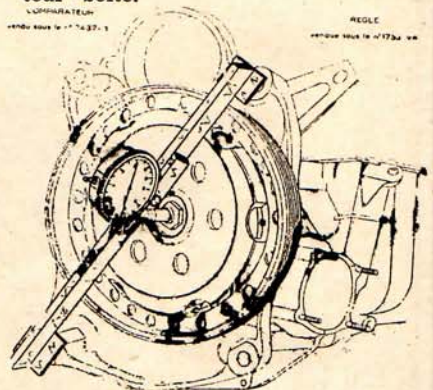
(ci-dessus). Régler de la position du tambour d'embrayage AZ.
